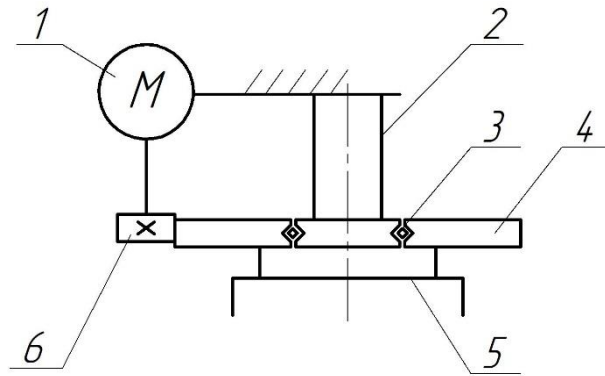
Кінематична схема механізму повороту спредера: 1 – мотор; 2 – рама перехідна; 3 – вузол опорний підшипниковий; 4 – вінець зубчастий; 5 – рама верхня (поворотна частина спредера); 6 – шестірня
